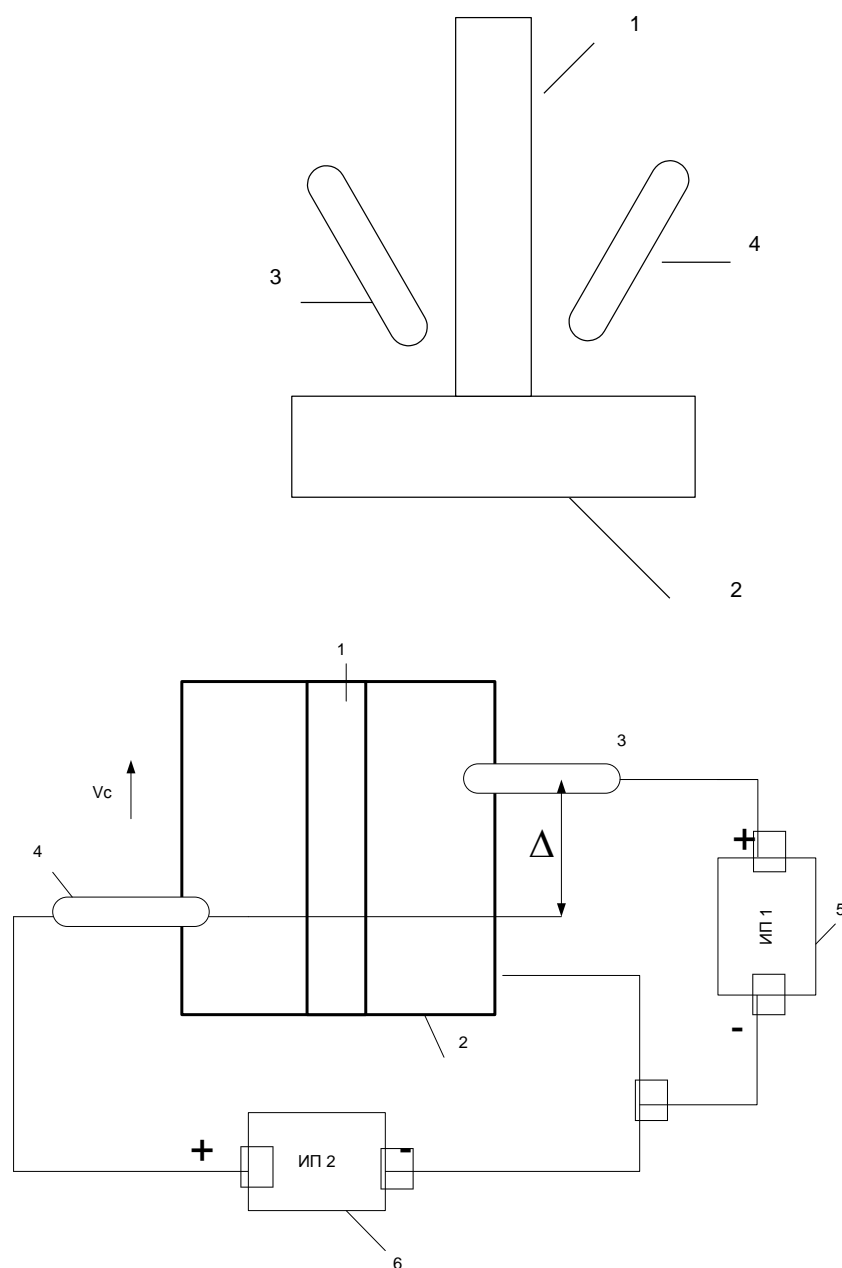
Схема выполнения предлагаемого способа сварки
